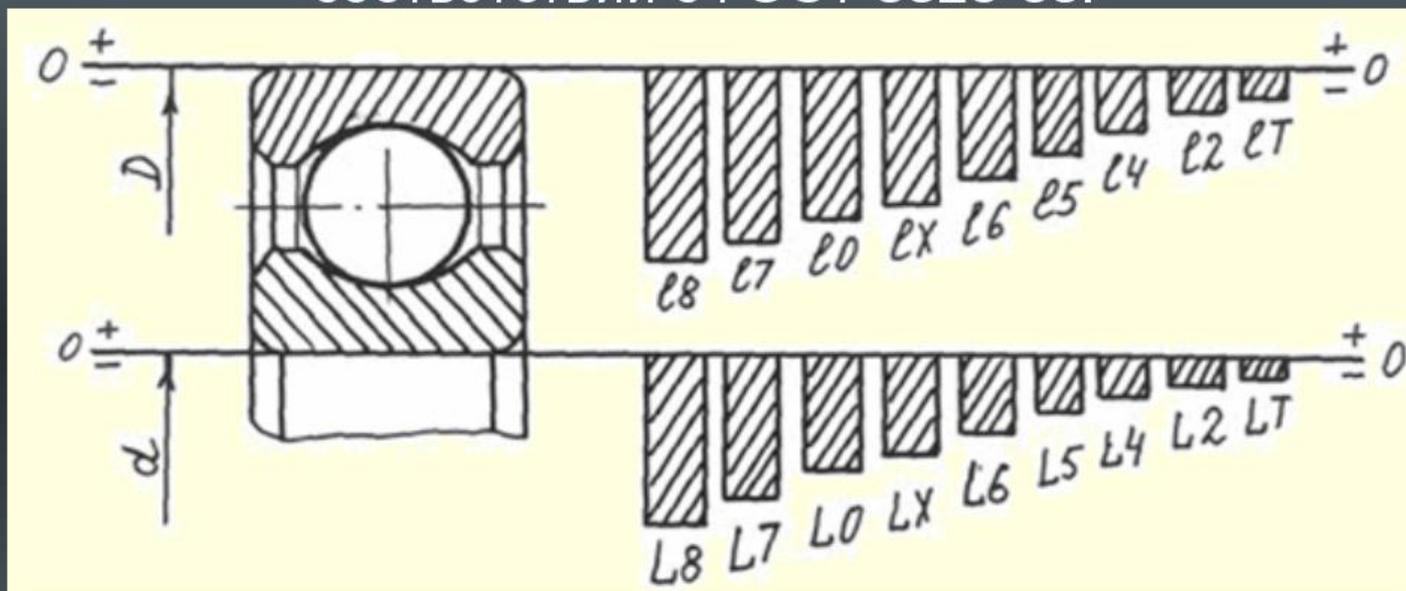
Обозначение допусков и посадок подшипника качения:
